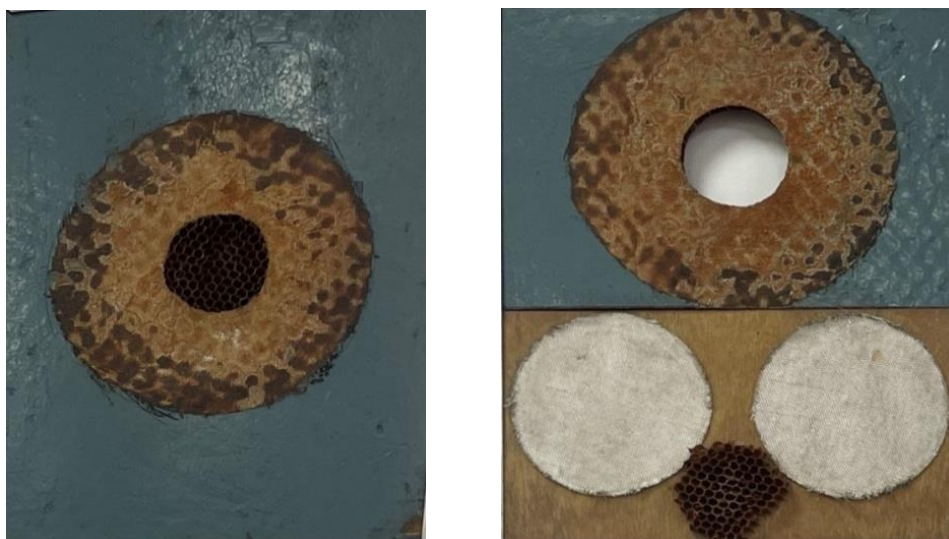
Ремонт трехслойной конструкции с сотовым наполнителем
